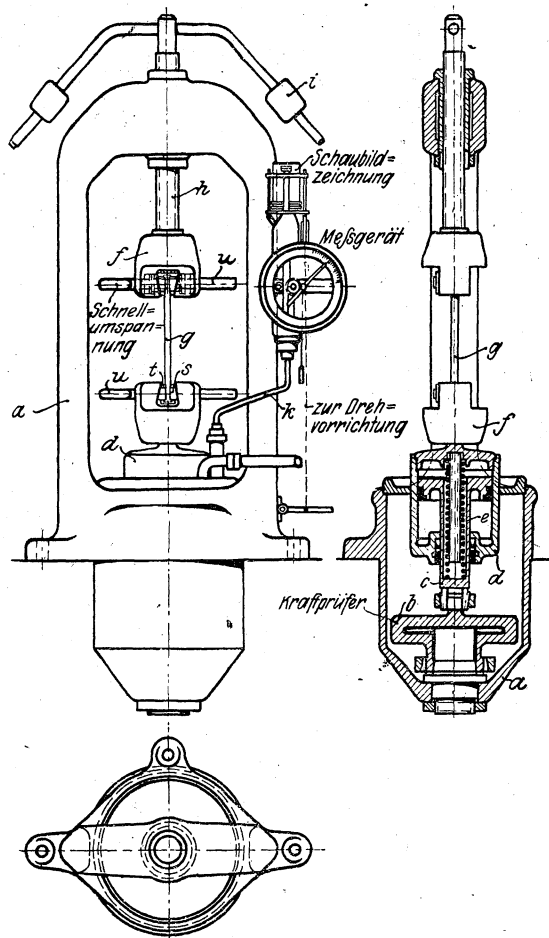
bis 9. 10 t-Maschine mit Kraftprüfer für Zug.
